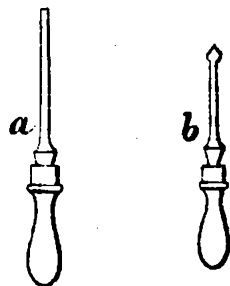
a) Ferro per bucare le fontane; b) Ferro per compr. il polverino.
